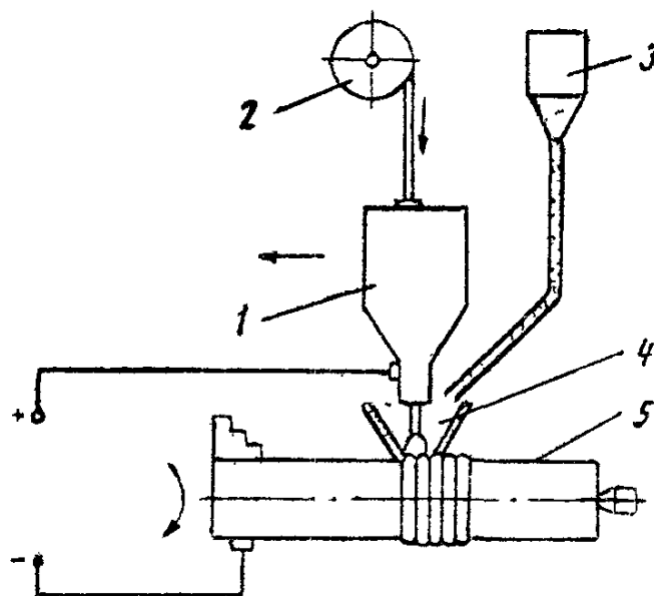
Принципова схема автоматичного електродугового наплавлення деталі під флюсом
